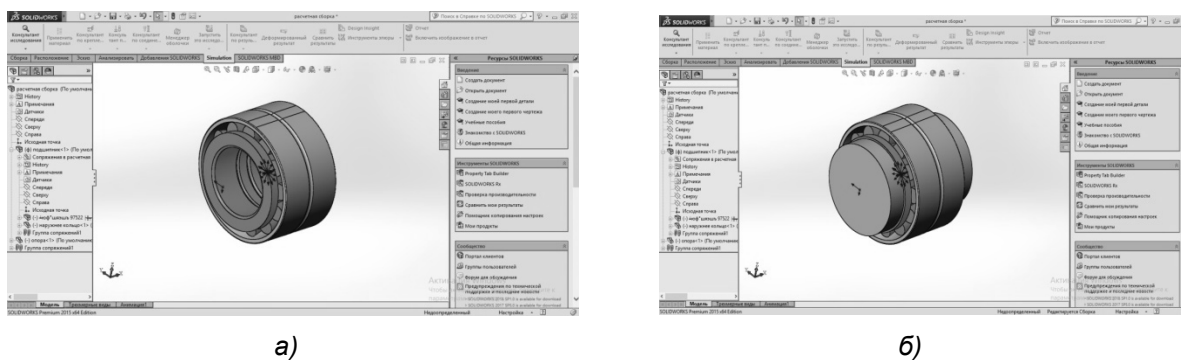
Расчетная схема для определения перемещений в SolidWorks: двухрядный радиальный подшипник (а); сборка подшипниковой опоры (б)
